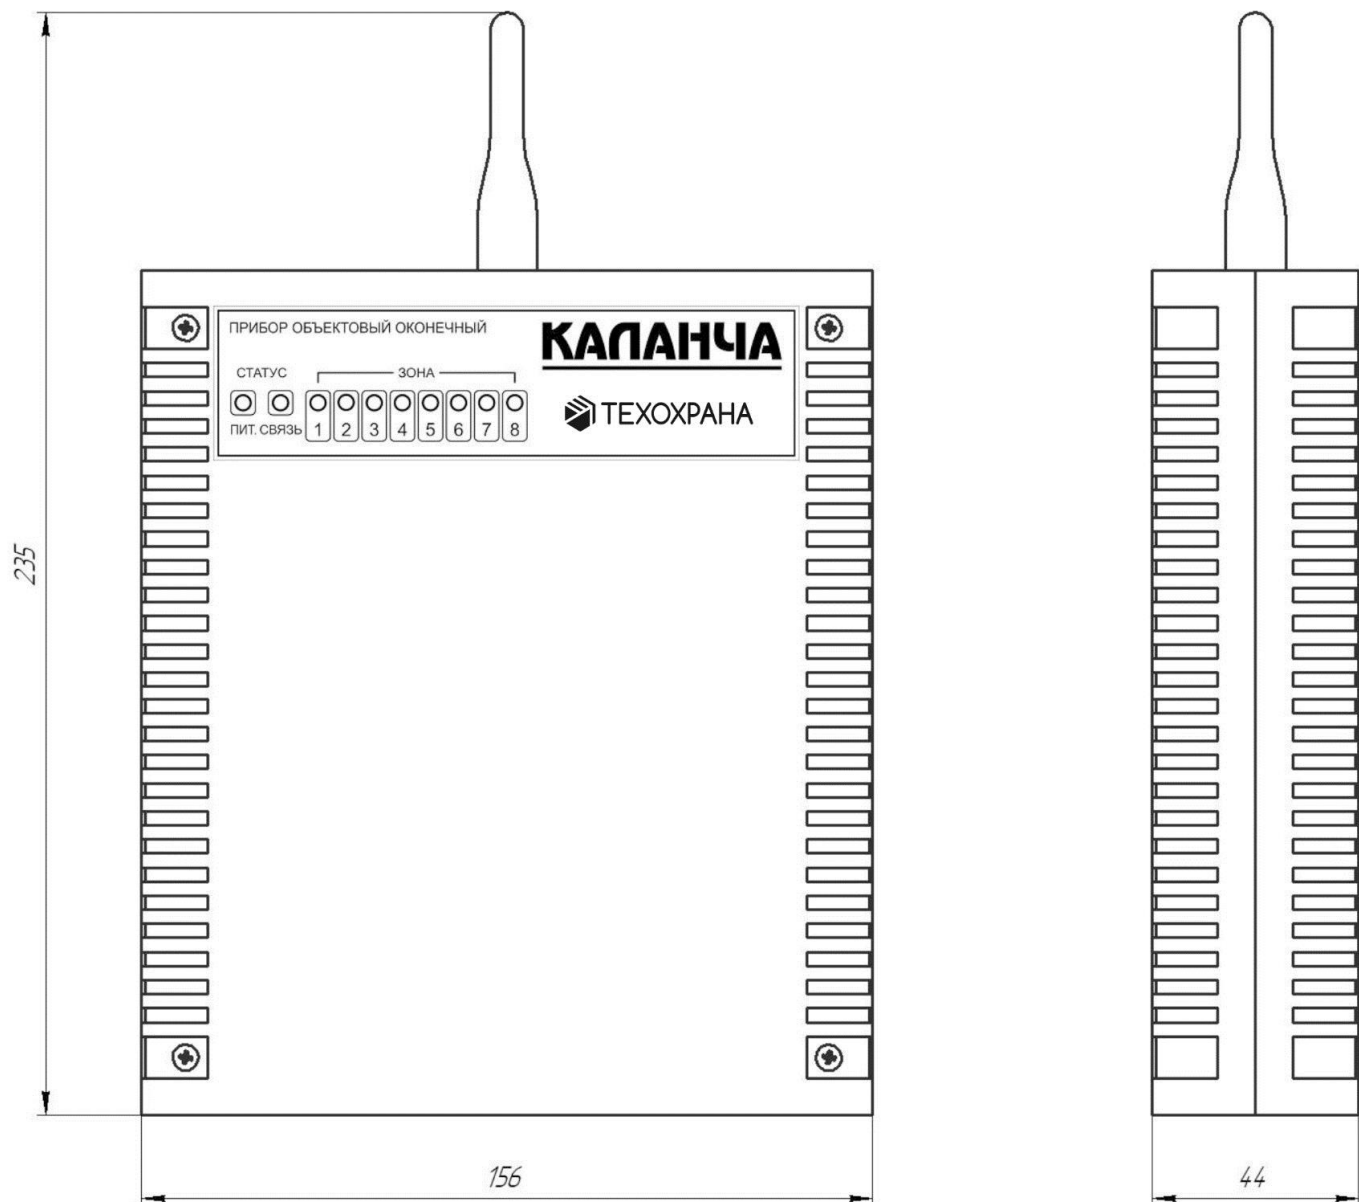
Внешний вид и установочные размеры ПОО «КАЛАНЧА»
